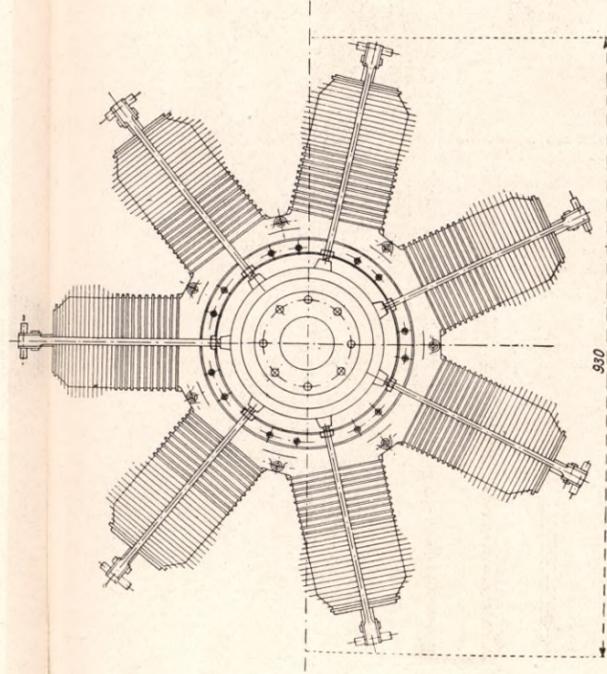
60 P 7-Zylindermotor, Raumzeichnung, Stirnansicht.
